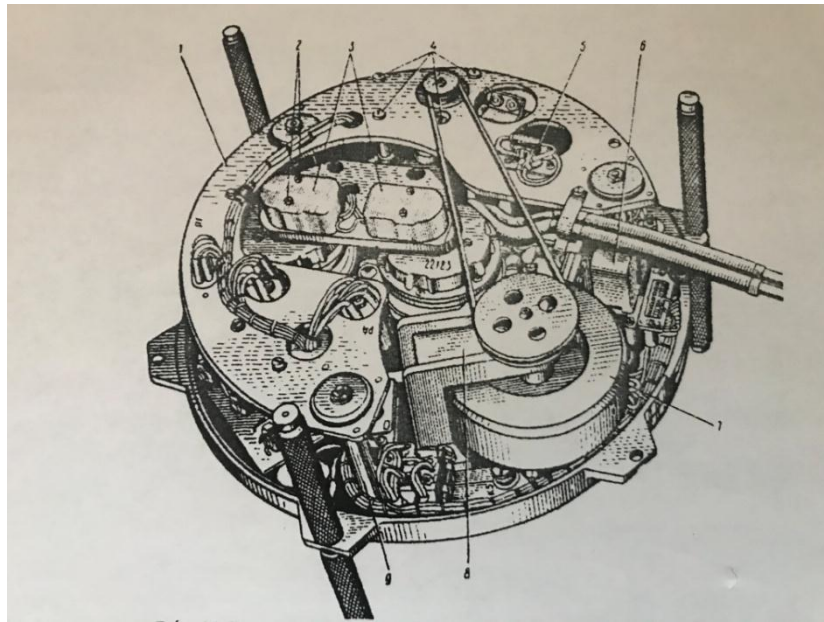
Стрічкопротяжний механізм на колонках (вид знизу). 1 – плата приводу; 2 – гвинти; 3 – кришки; 4 – гвинти для кріплення редуктора до плати приводу; 5 – колодка; 6 – реле; 7 – маховик; 8 – кронштейн для кріплення маховика; 9 – стійка плати приводу.
